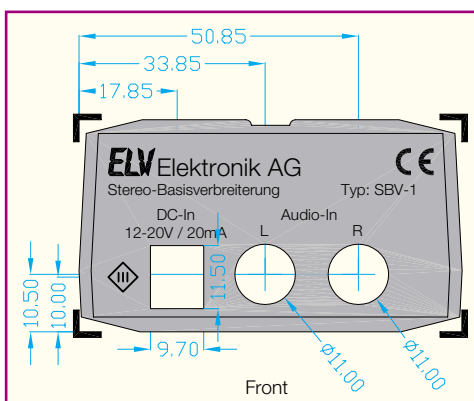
Maßzeichnung und Bedruckung der Gehäusefront
